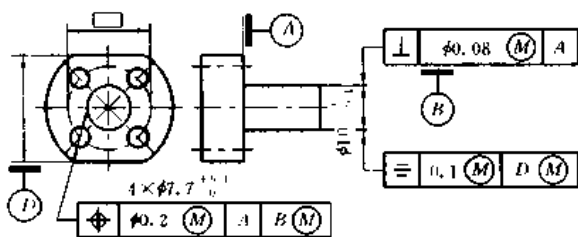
表示基准 B 本身采用最大实体要求的直线度公差,且基准 B 的基准符号直接标注在形成该最大实体实效边界的形位公差框格下面,其边界尺寸等于相应的最大实体尺寸加直线度公差。
